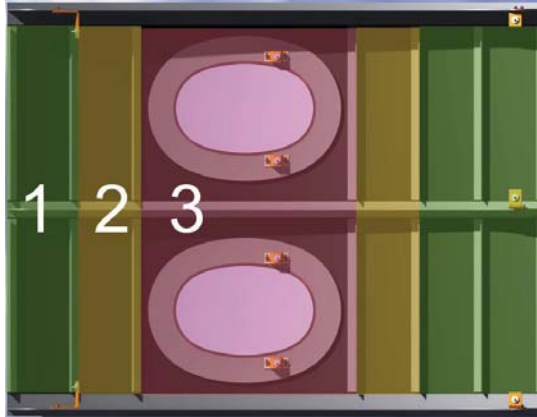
Draufsicht der CFK-Rumpfstruktur mit den farblich gekennzeichneten Bereichen 1, 2 und 3 unterschiedlicher Hautdicke und den Lagerungspunkten für das Lining (orange) an den Spanten und auf den Fensterrahmen.
